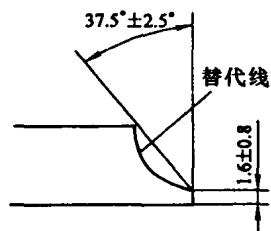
钨极弧焊根部焊道的焊缝斜角
